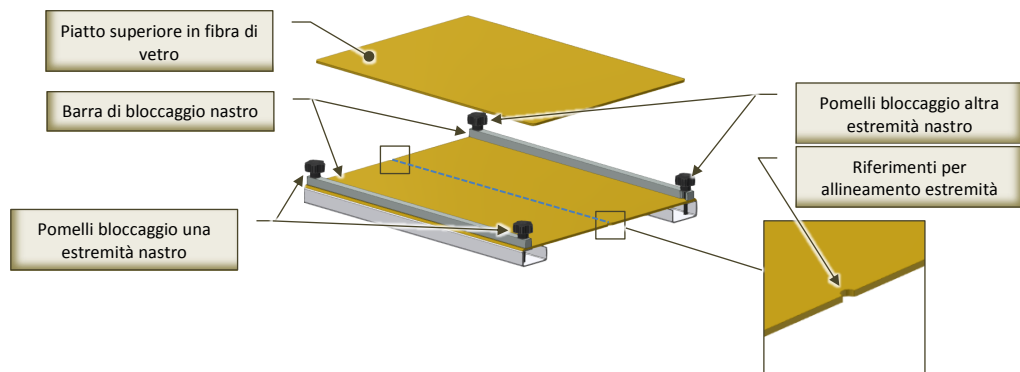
Posizionamento nastro Fabric su piastra di giunzione (parti)
